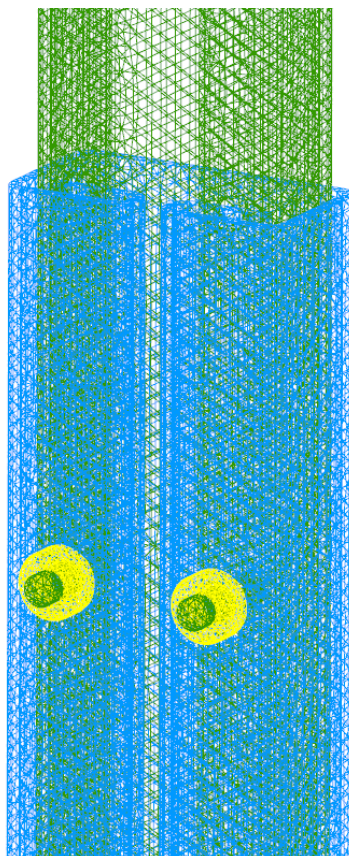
Detalle mallado del utillaje y elementos de unión.
